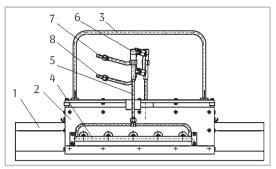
Чертеж переносной установки для нагрева рельсового пути УНР-ЖД
